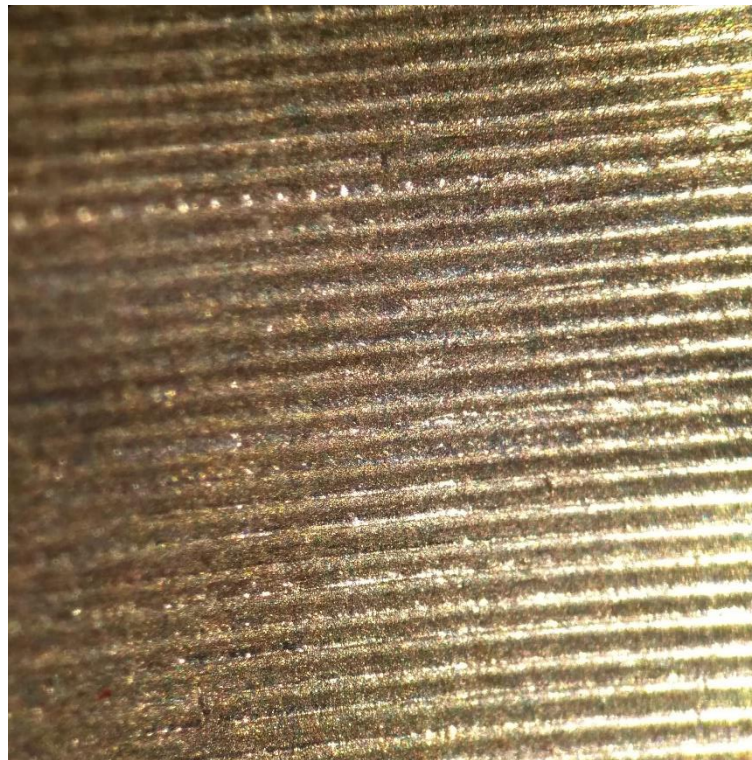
Superfície da bucha recém usinada (Fonte: Autores)
